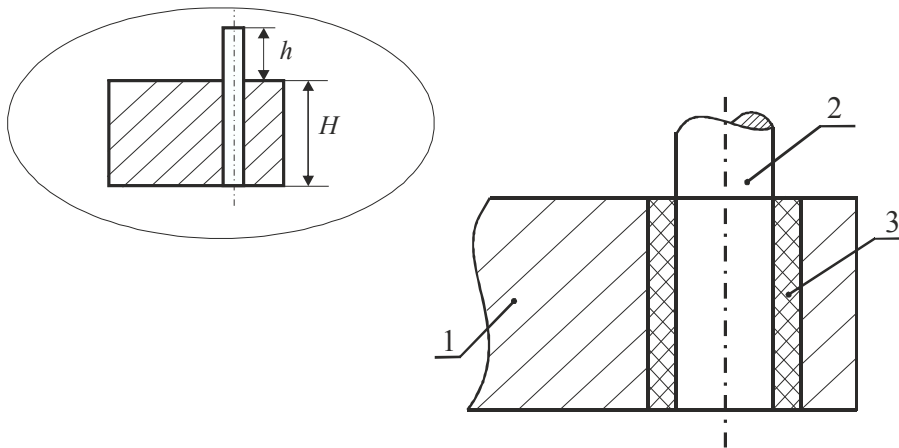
Схема соединения колонки с базовой плитой: 1 – нижняя базовая плита; 2 – направляющая колонка; 3 – полимерный материал
